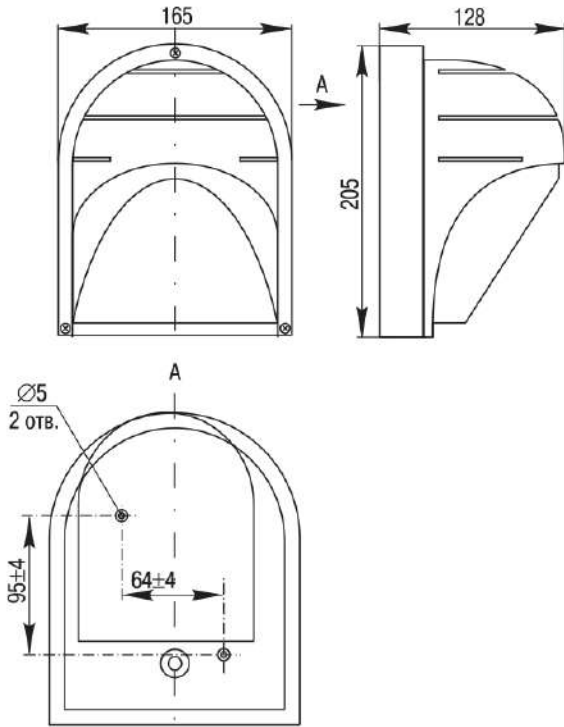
Габаритные и установочные размеры светильника НПП 2501
